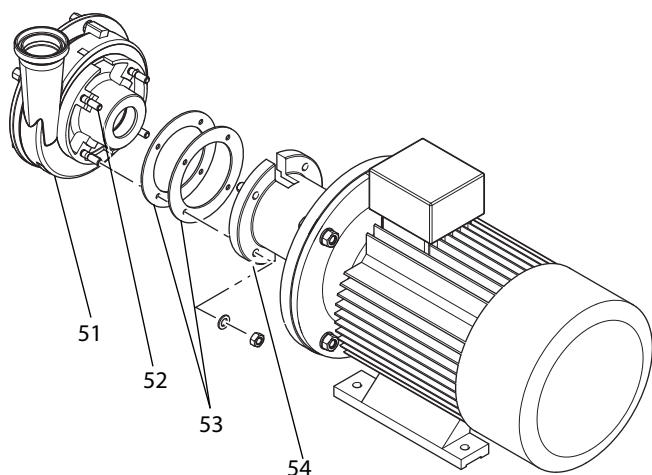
Montar a caixa da bomba no caso de junta flangeada
